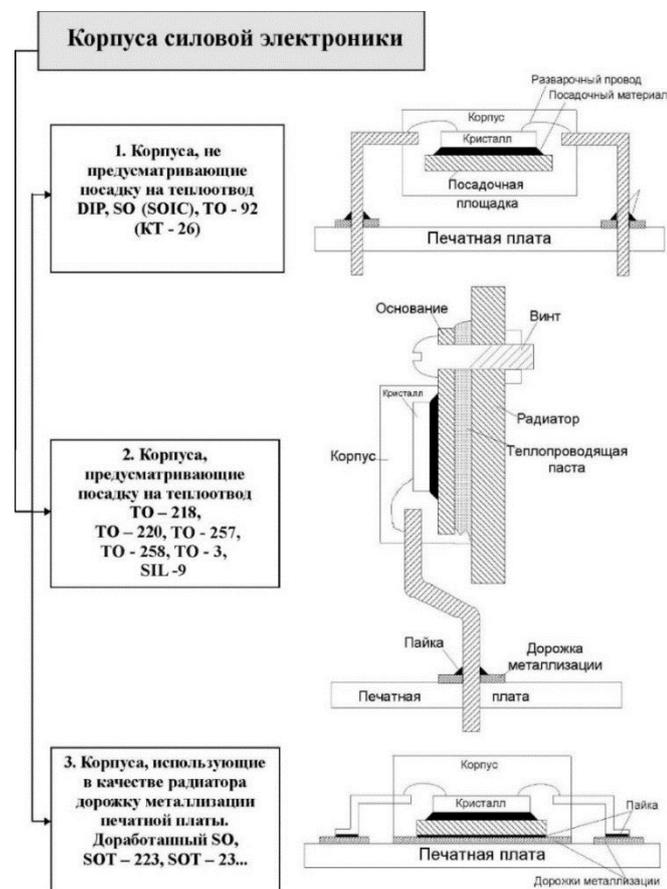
Основные типы корпусов для полупроводниковых приборов и ИМС силовой электроники
